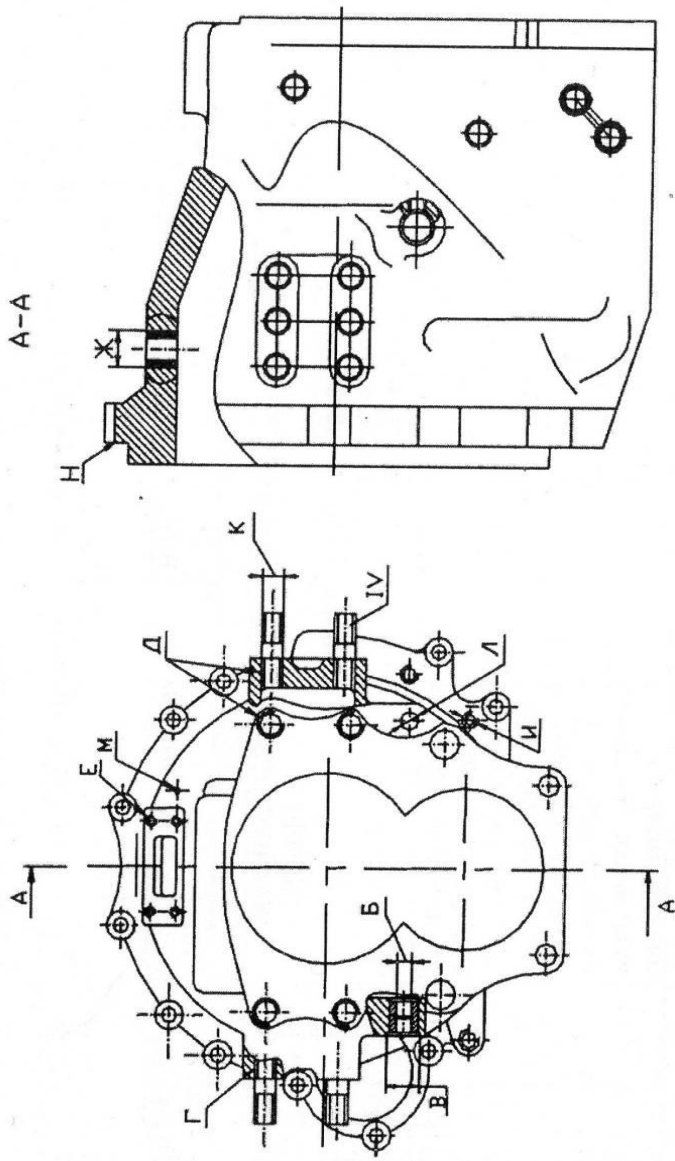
Картер делителя передач автомобиля КАМАЗ
